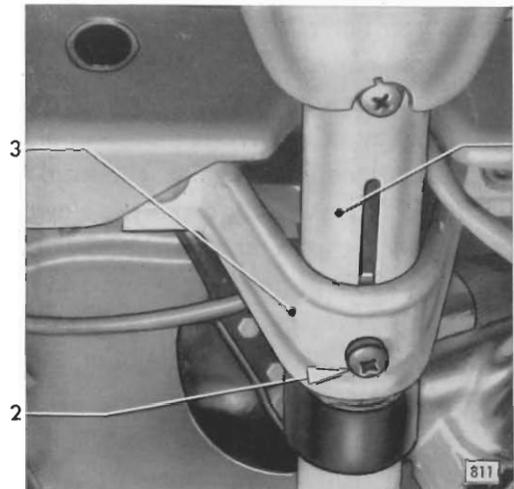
Befestigungsschraube für Lenkspindelbuchse in Haltebügel für Lenkstützrohr
